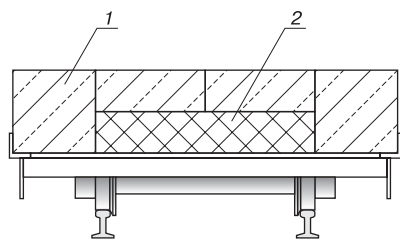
Футеровка вагона туннельной печи: 1 – блоки рабочего слоя футеровки; 2 – теплоизоляционный слой
